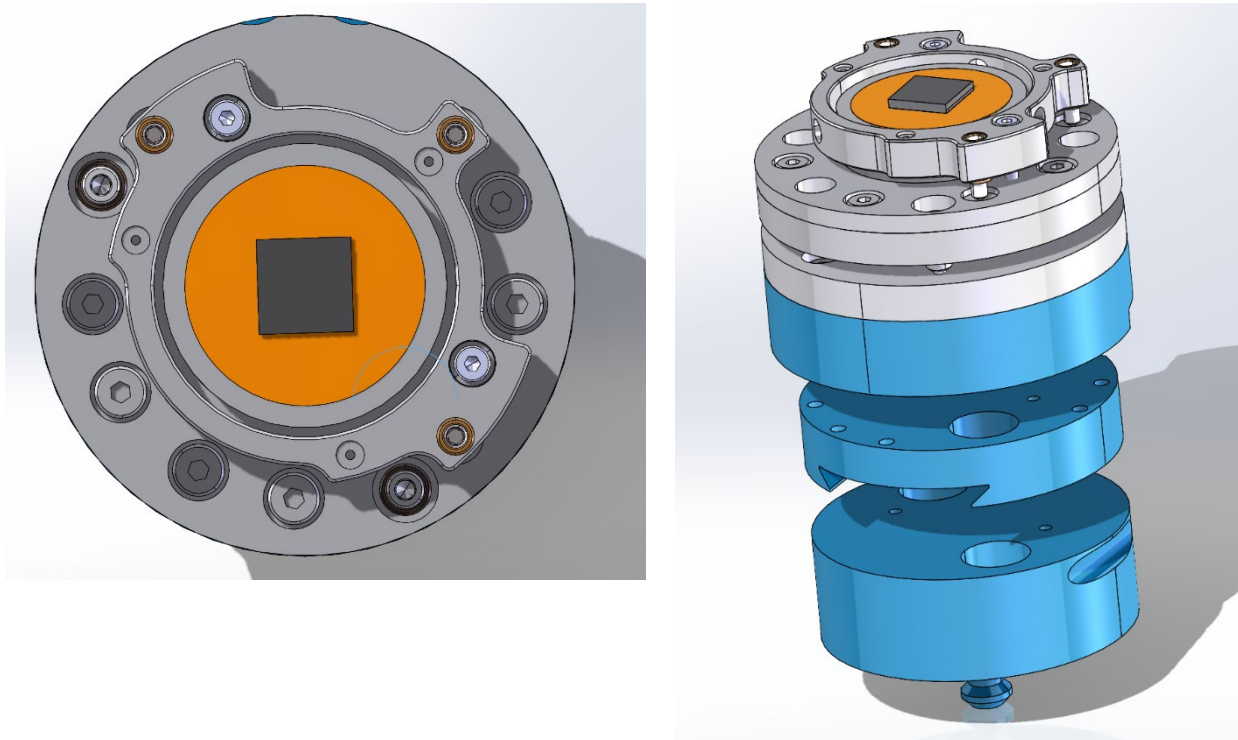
Konstruktionszeichnung des neuen Probenhalters V1, Draufsicht (Bild links) und Seitenansicht des CAD-Modells (Bild rechts)
